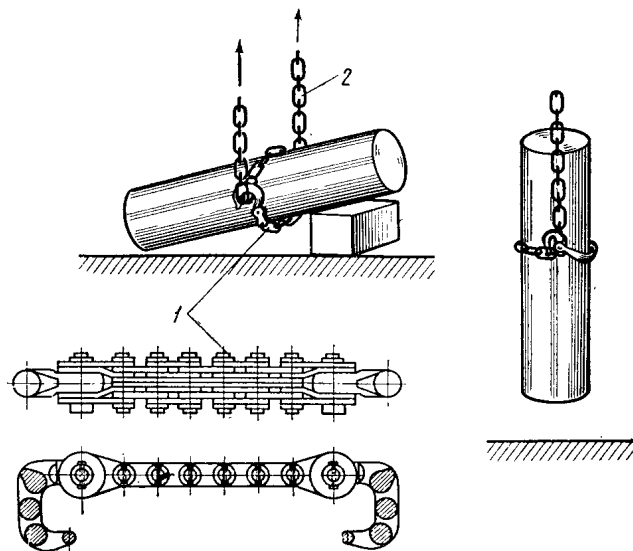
Схема поворота заготовки в вертикальное положение при помощи гибкой скобы и цепи:
